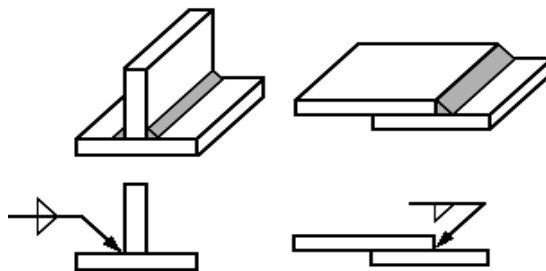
Soldadura de Filete.<sup>11</sup>
